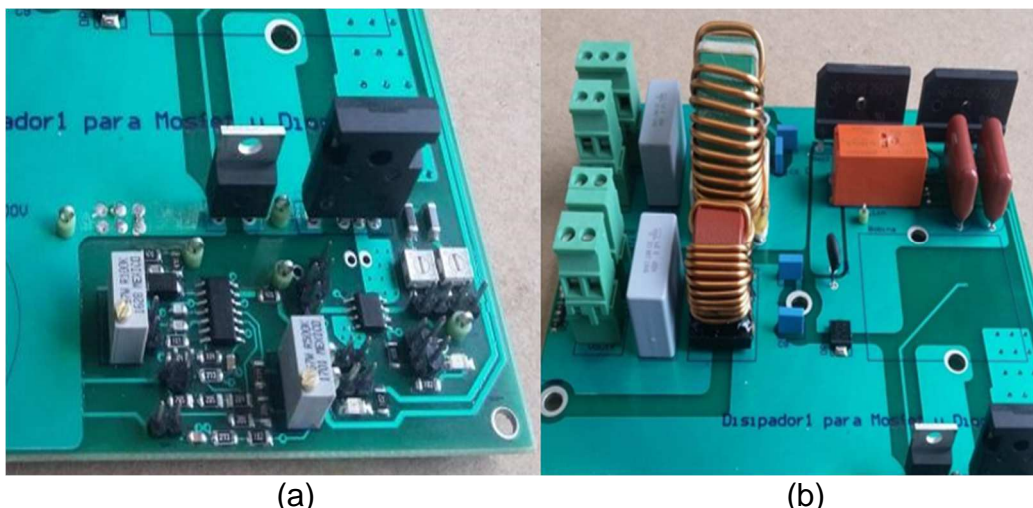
Montaje y soldadura de los componentes en las áreas del (a) del PFC y circuito de control (b) y de componentes de potencia.
